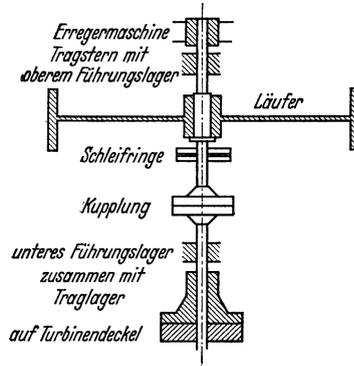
Läufer mit einem oberen Führungslager, Traglager und unteres Führungslager auf Turbinendeckel, Erregermaschine aufgebaut.
